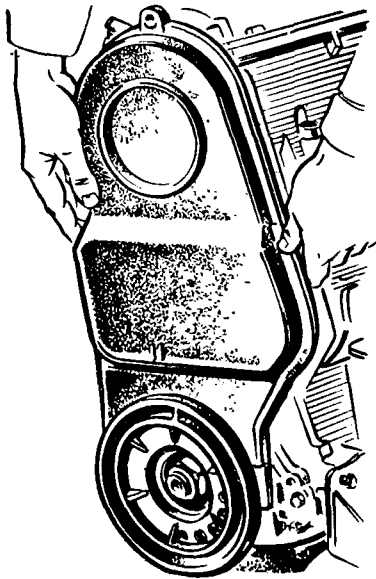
Снятие верхнего кожуха плоскозубчатого ремня
